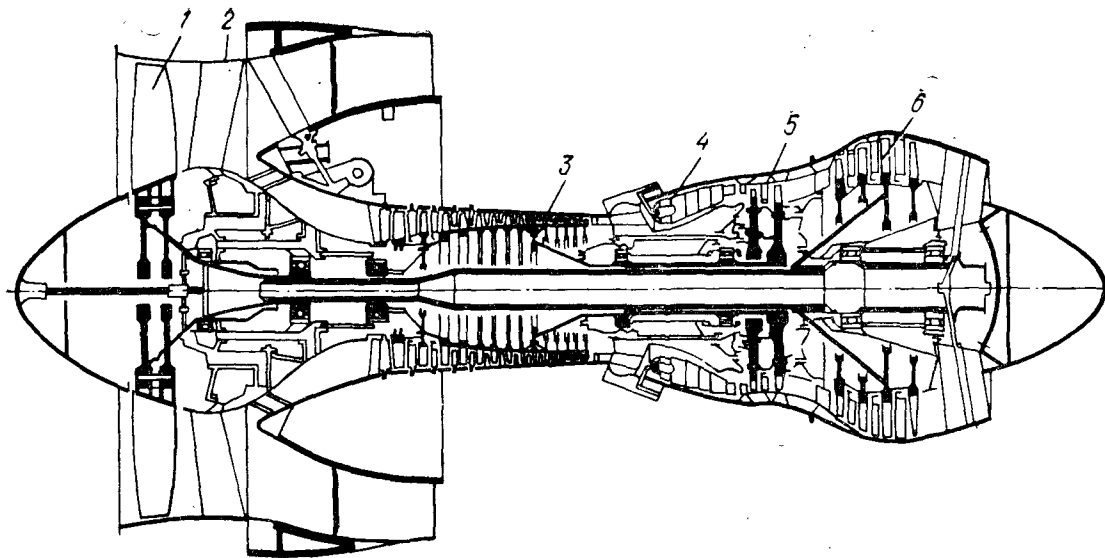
Конструктивная схема двигателя TF34-GE-2:
